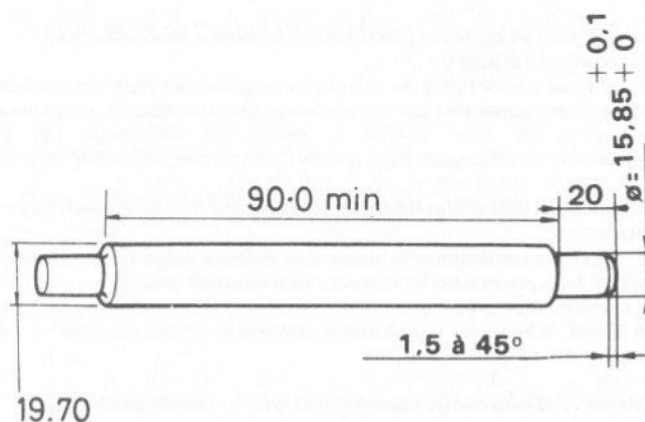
Dimensions (en mm) de l'outil de centrage d'embrayage du moteur TU (Sec 11)
